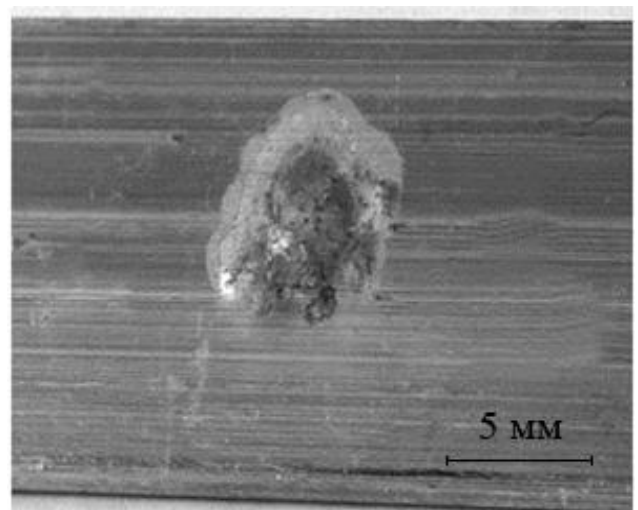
Одиночный очаг расслаивающей коррозии
